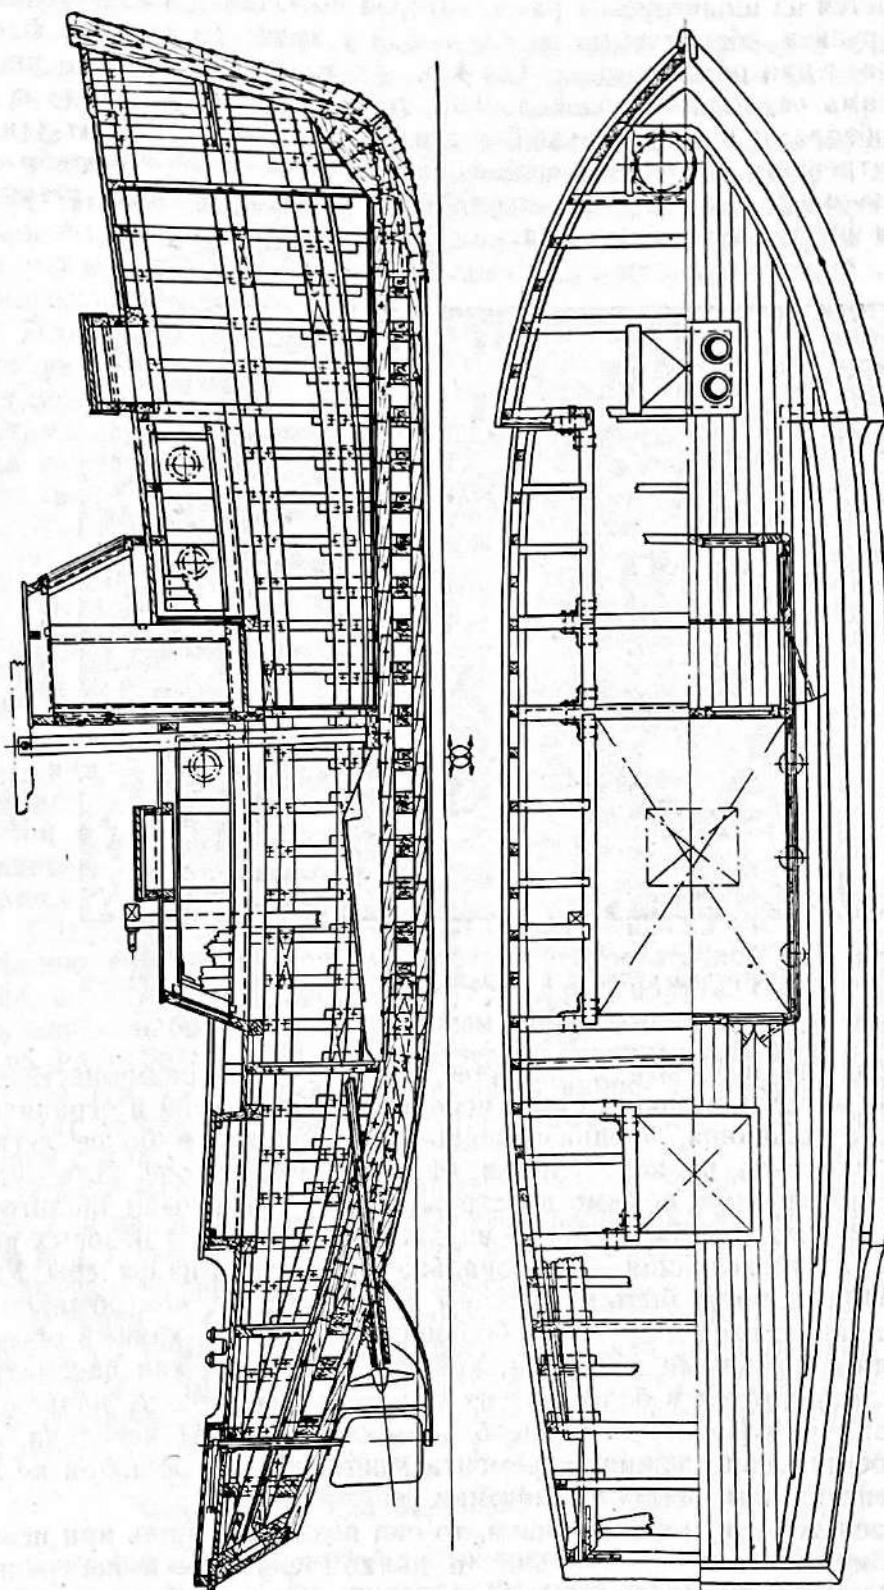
Конструктивный продольный разрез и план палубы буксирного катера.
